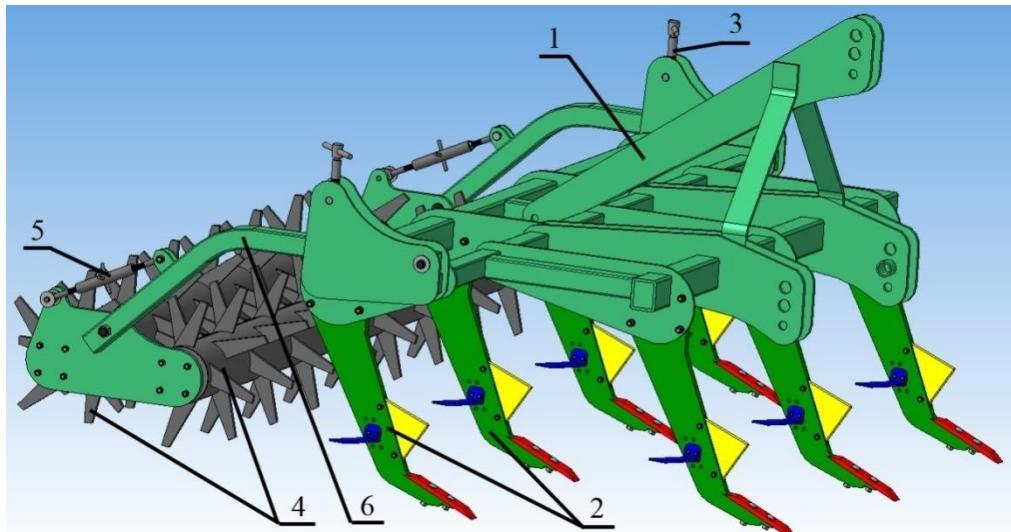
Загальний вигляд комбінованого чизеля: 1 – рама; 2 – лапа чизельна; 3 – регулювальний механізм; 4 – спарений зу- бчастий коток; 5 – гвинт; 6 – механізм кріplення котка
